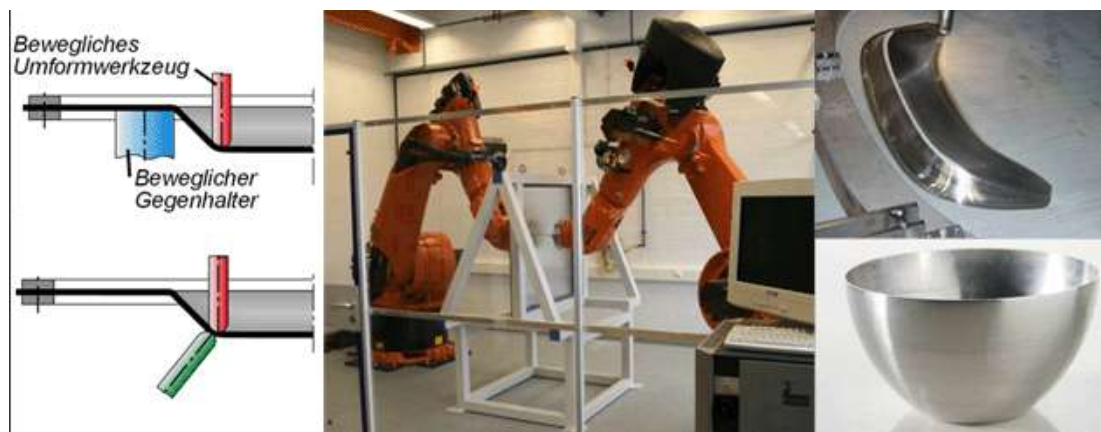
Piezas fabricada mediante el sistema Roboforming. (fuente: [a])
